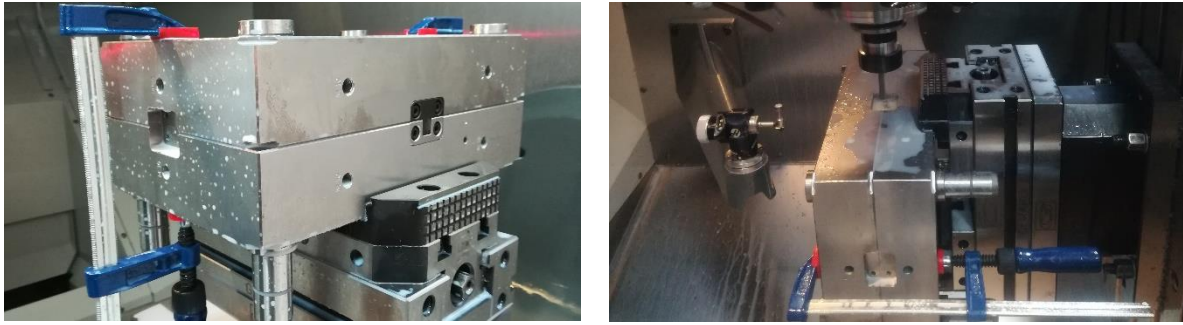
Maquinagem das caixas dos *interlocks*.
